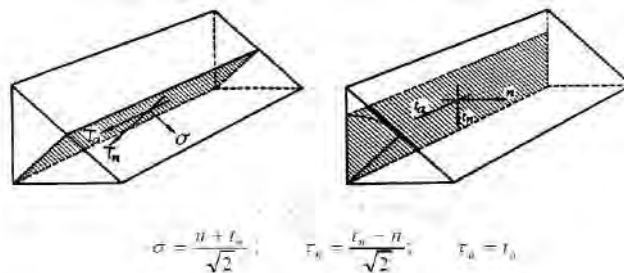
Planos y tensiones de la garganta de soldadura.
